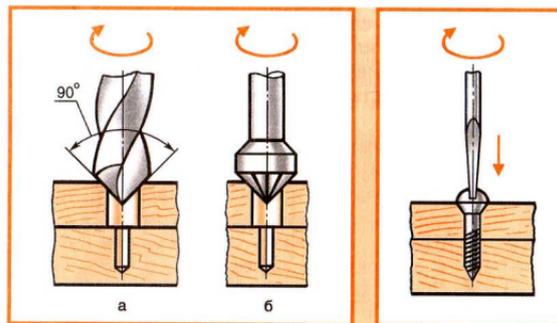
Подготовка гнезда под головку шурупа сверлом (а) или зенковкой (б)
